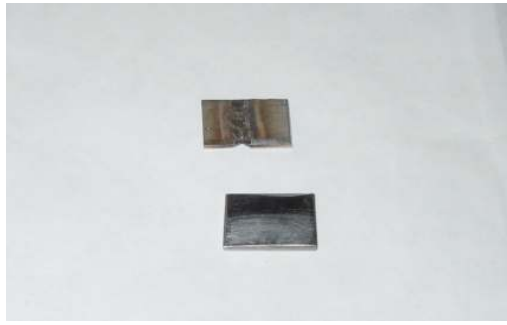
Aciers inoxydables austénitiques. Soudé & non soudé
